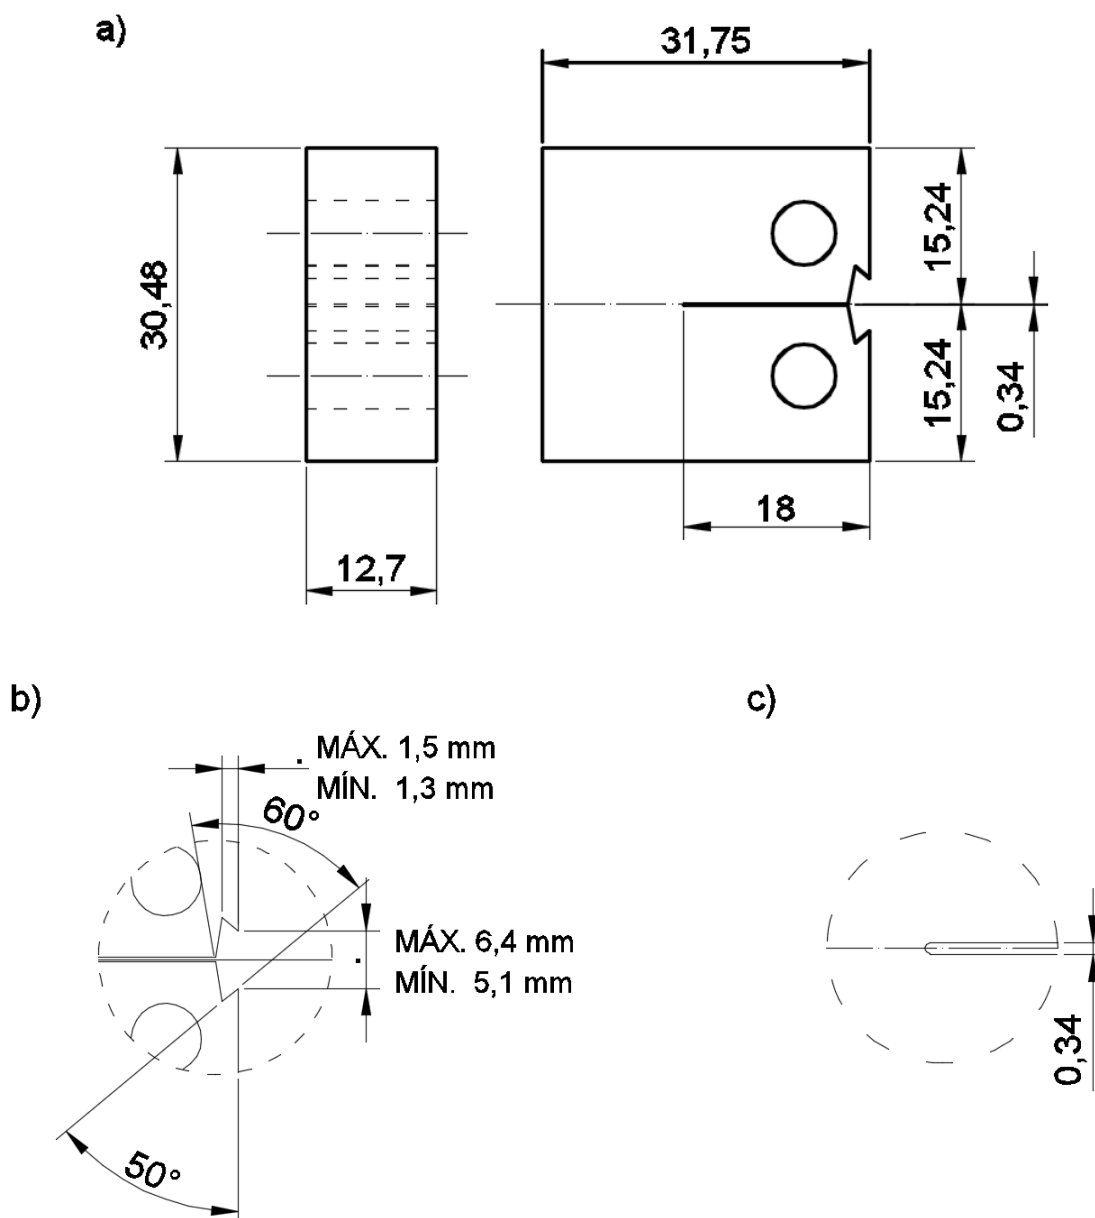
a) Dimensões do corpo de prova de tenacidade; b) detalhe do recorte na peça para fixação do sensor (*clip gage*); e c) detalhe do fundo arredondado do entalhe. Todas as dimensões em milímetros.
